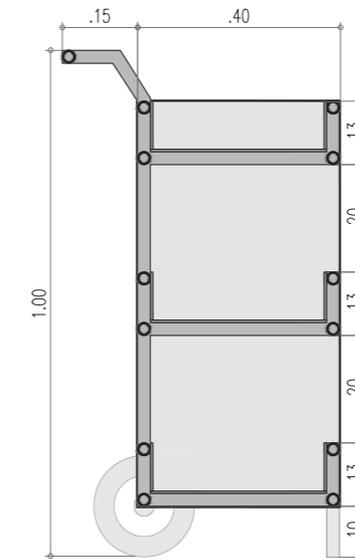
Sección puesto de venta ambulante tipo 3. Esc 1:15
